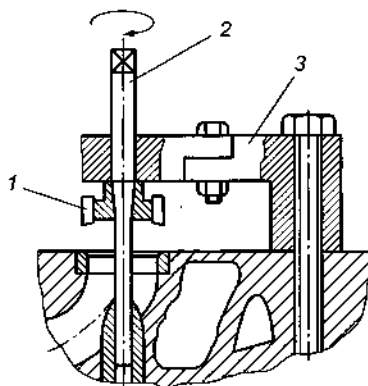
Приспособление для растачивания седла или его гнезда: 1 — головка с регулирующими резцами; 2 — пилот; 3 — кронштейн регулируемой длины для крепления на головке
